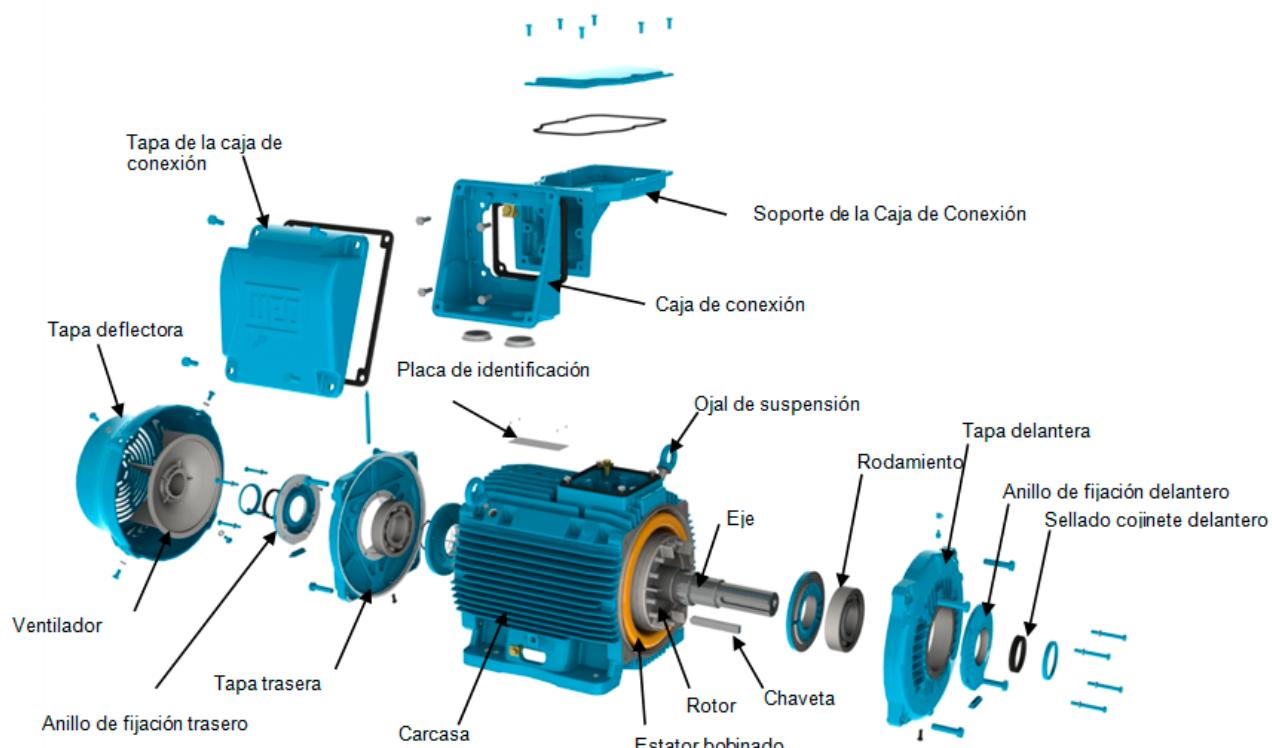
Vista explotada de los componentes de un motor W22.
